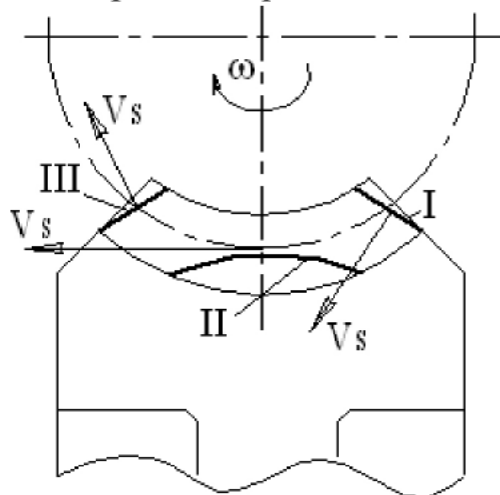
Линия контакта зуба колеса и витка червяка
